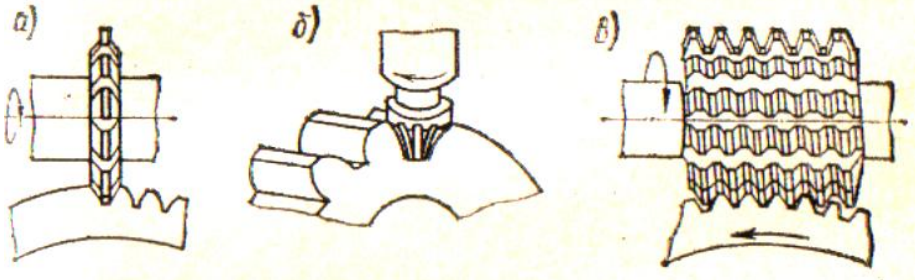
Схемы обработки зубчатых колёс : а-модульной дисковой фрезой; б- пальцевой фрезой; в- нарезание зубчатых колёс червячной фрезой (огибанием)
